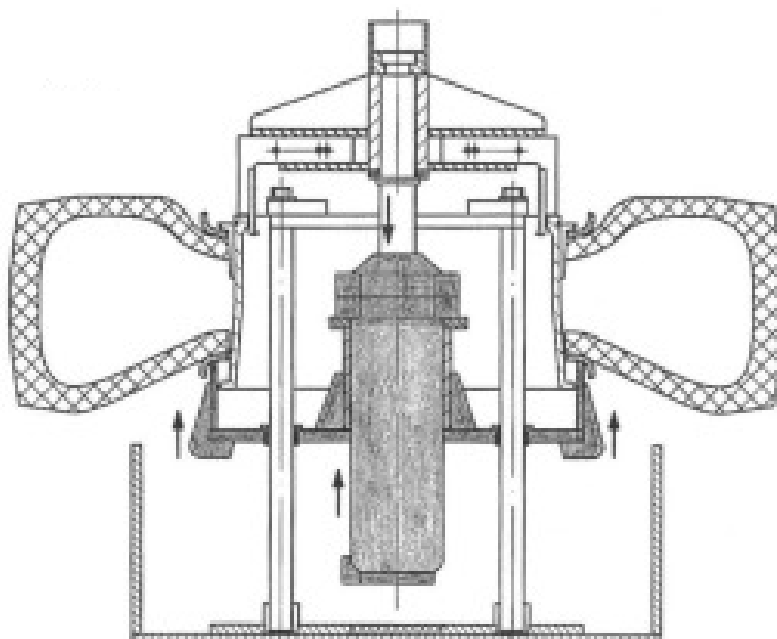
Общий вид шиномонтажного стенда для демонтажа грузовых колёс с разборным диском
